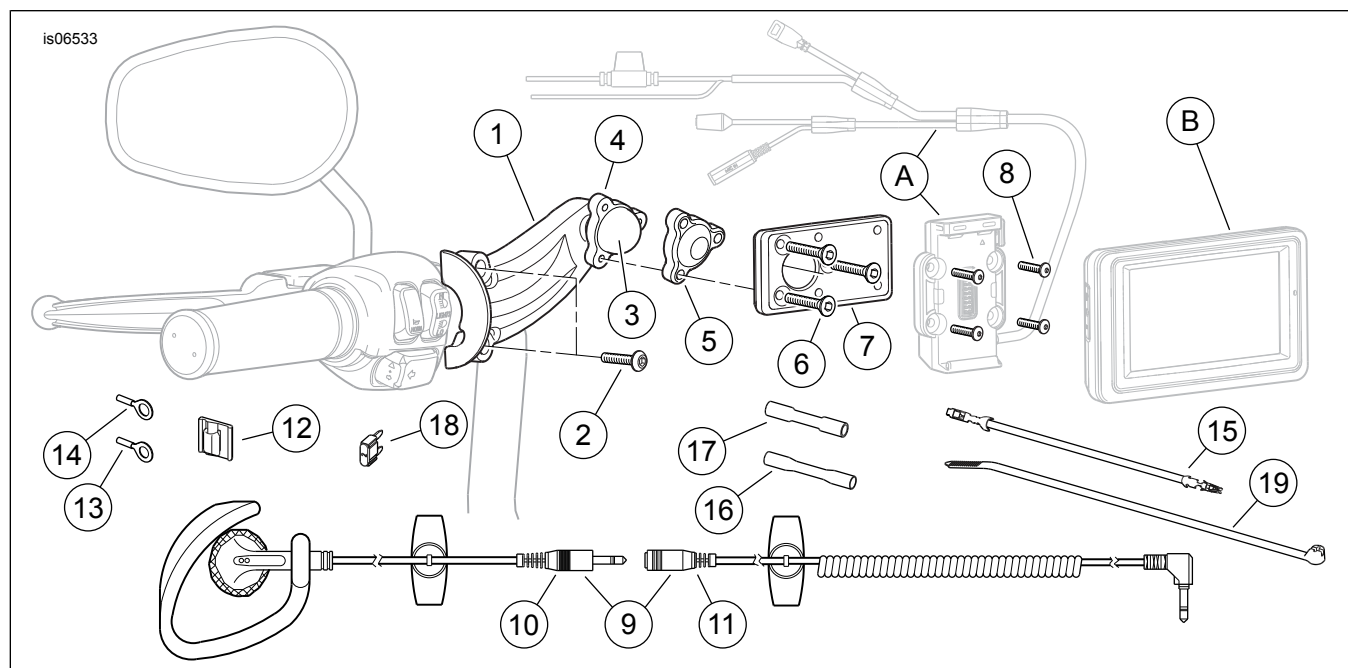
Peças de reposição, kit de GPS Road Tech Zumo 660 e Zumo 665 para instalação em guidom
